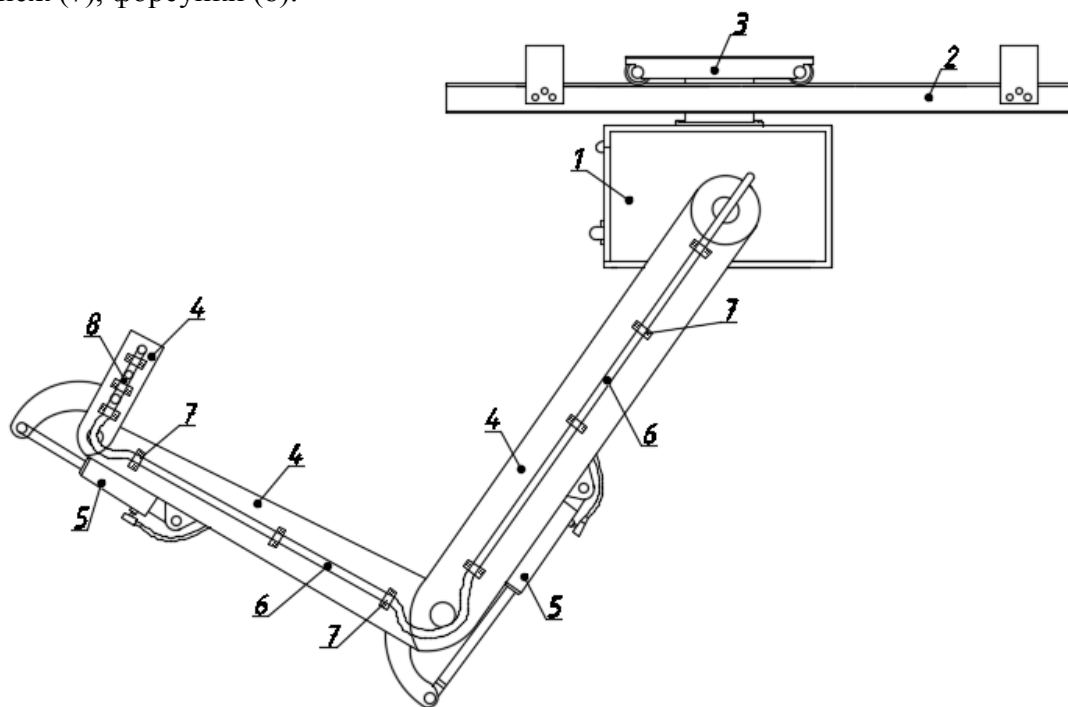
Эскиз роботизированного устройства: 1 – корпус устройства; 2 – железный рельс; 3 – ходовая каретка; 4 – каркас манипулятора; 5 – гидроцилиндры; 6 – шланг; 7 – крепеж; 8 – форсунки.
